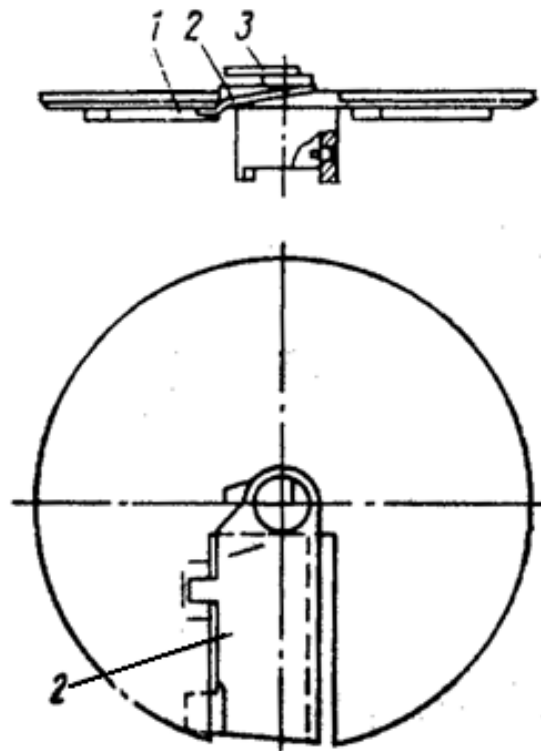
Будова робочого органу верхнього диска подрібнювача з ножом: 1 - диск; 2 - ніж змінний; 3 - спеціальний болт для закріплення ножа.
